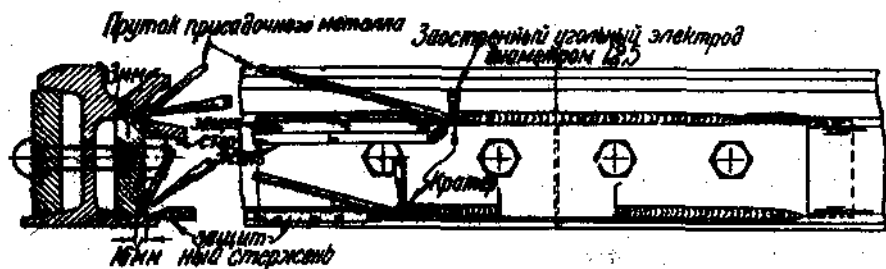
Сварка стыков рельс по способу Уна.
